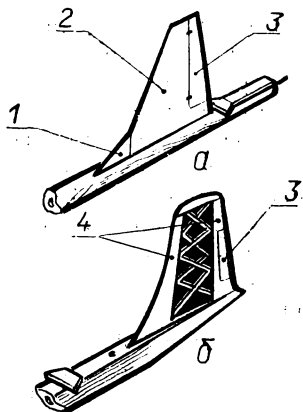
Конструкции килей: а — из пластины, б — наборная конструкция; 1 — форкиль, 2 — средняя часть, 3 — руль направления, 4 — кромки.
